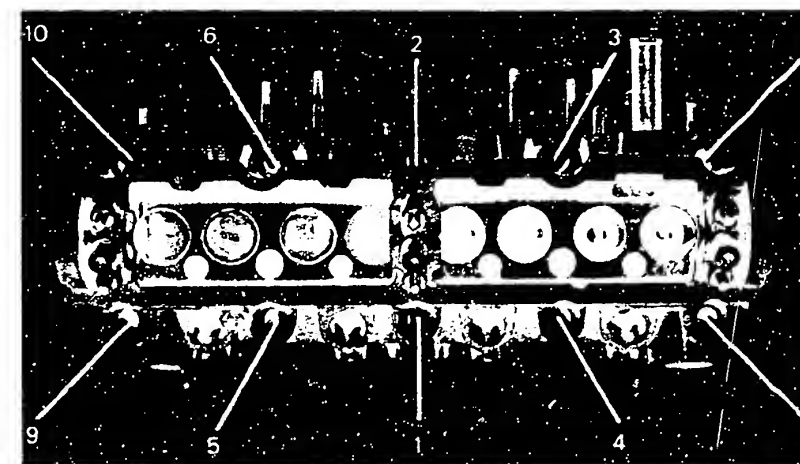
Beim Dieselmotor sind die Zylinderkopfschrauben nach dem Reinigen mit Molybdämfett zu schmieren und in der gezeigten Reihenfolge anzuziehen.
